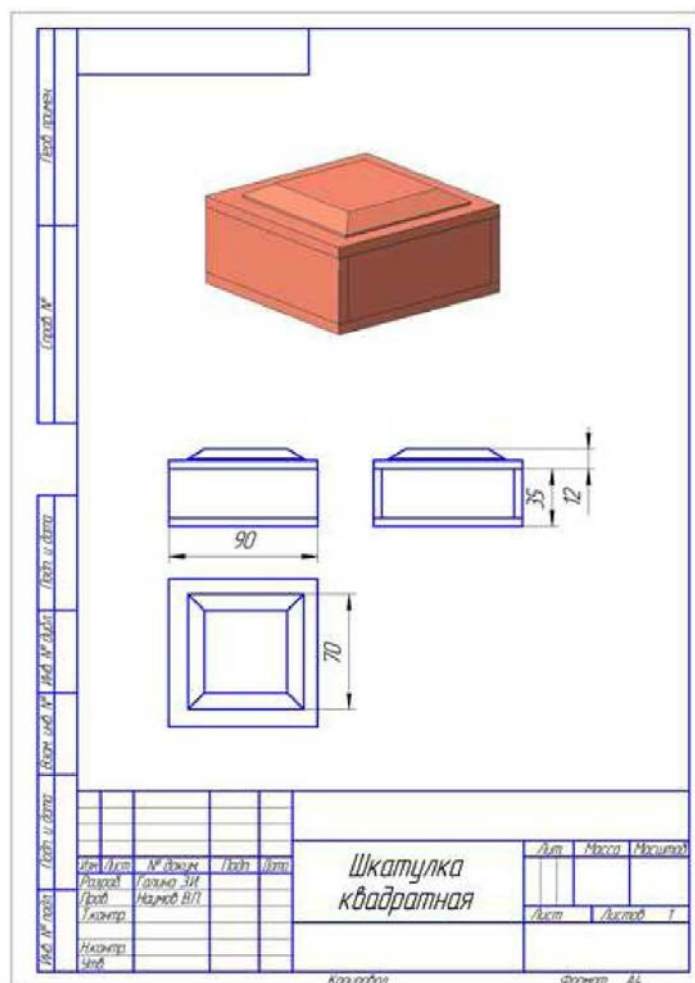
Общий вид и чертеж декоративной шкатулки из поделочного камня
